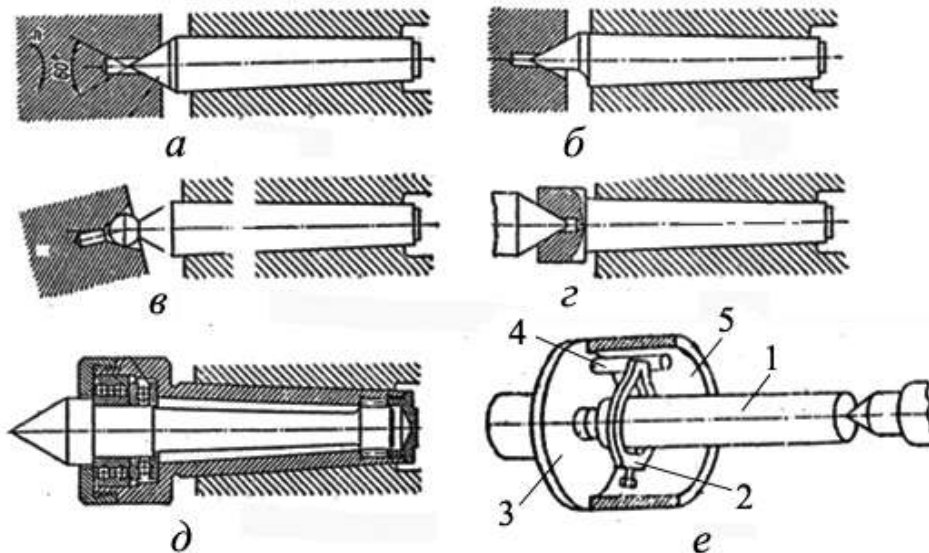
Задні центри (а...д) і повідковий патрон (е) для обробки довгих заготовок на токарних верстатах
